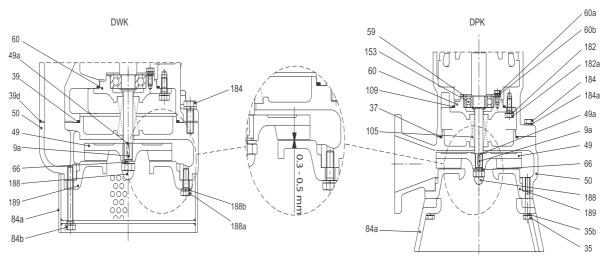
Сборка рабочего колеса и корпуса насоса и зазор щелевого уплотнения рабочего колеса
